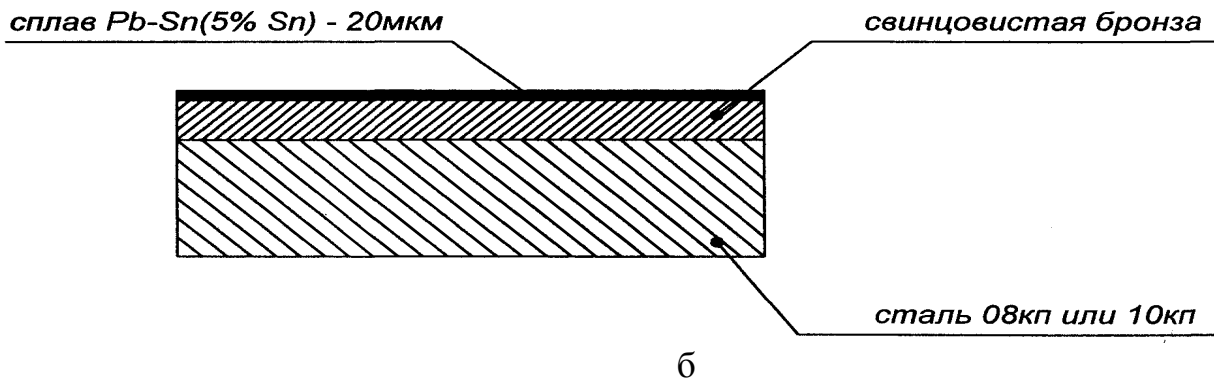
Схема строения вкладыша подшипника скольжения
